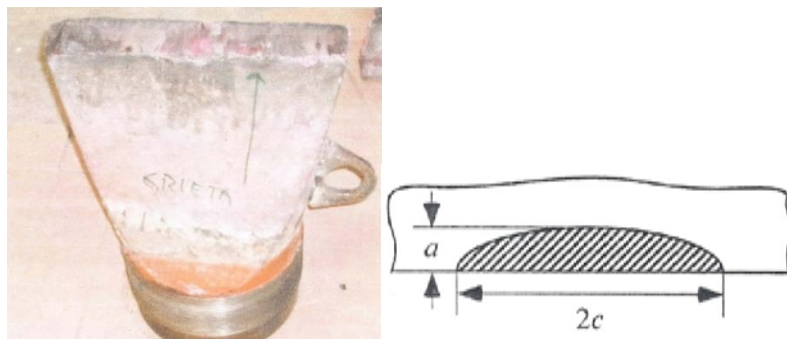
Grieta encontrada en anclaje [12] y geometría de la grieta.
